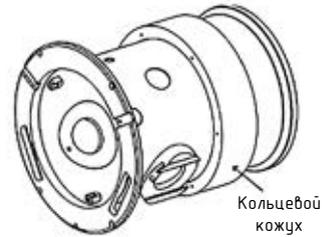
Расположение отверстий для выпуска технологических газов при сварке экрана с кожухом
